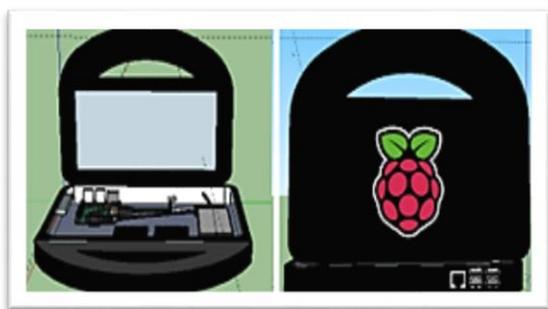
Diseño de la vista frontal y posterior en SketchUp
